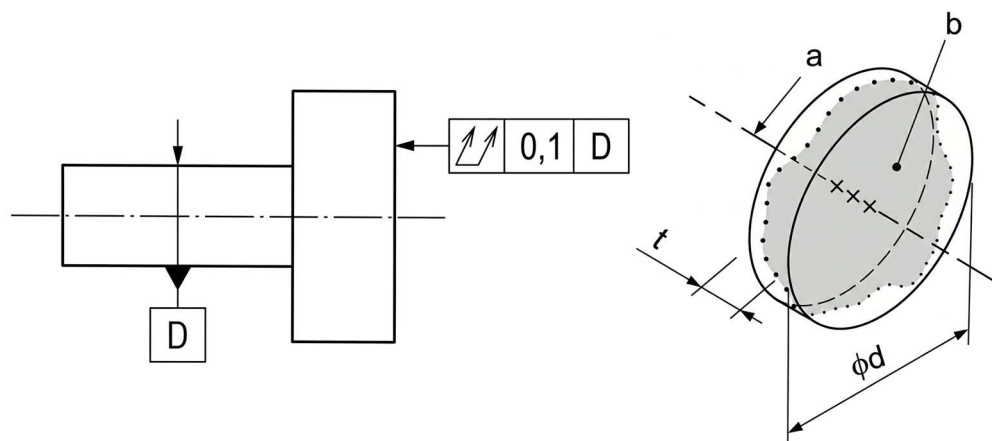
Indikace kruhového čelního házení a její toleranční pole [8]
